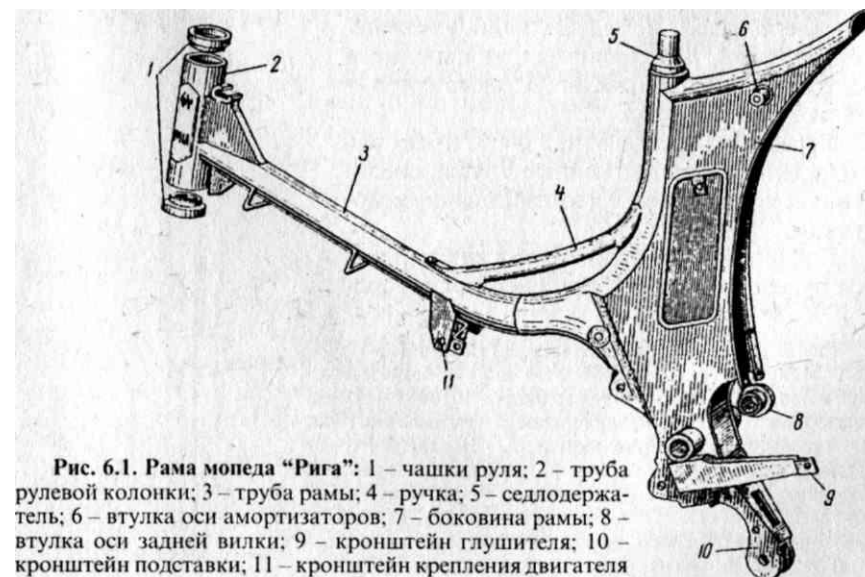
Рама мопеда "Рига": 1 - чашки руля; 2 - труба рулевой колонки; 3 - труба рамы; 4 - ручка; 5 - седлодержатель; 6 - втулка оси амортизаторов; 7 - боковина рамы; 8 - втулка оси задней вилки; 9 - кронштейн глушителя; 10 - кронштейн подставки; 11 - кронштейн крепления двигателя
